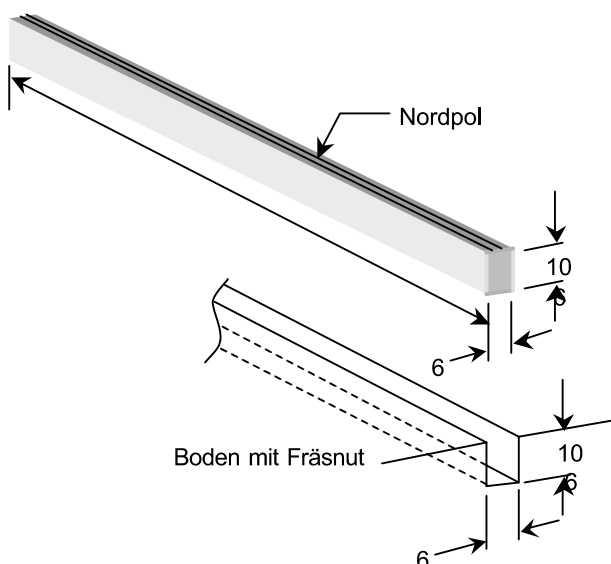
Abmessungen des eingefrästen Magnetbands und der Fräsnut
